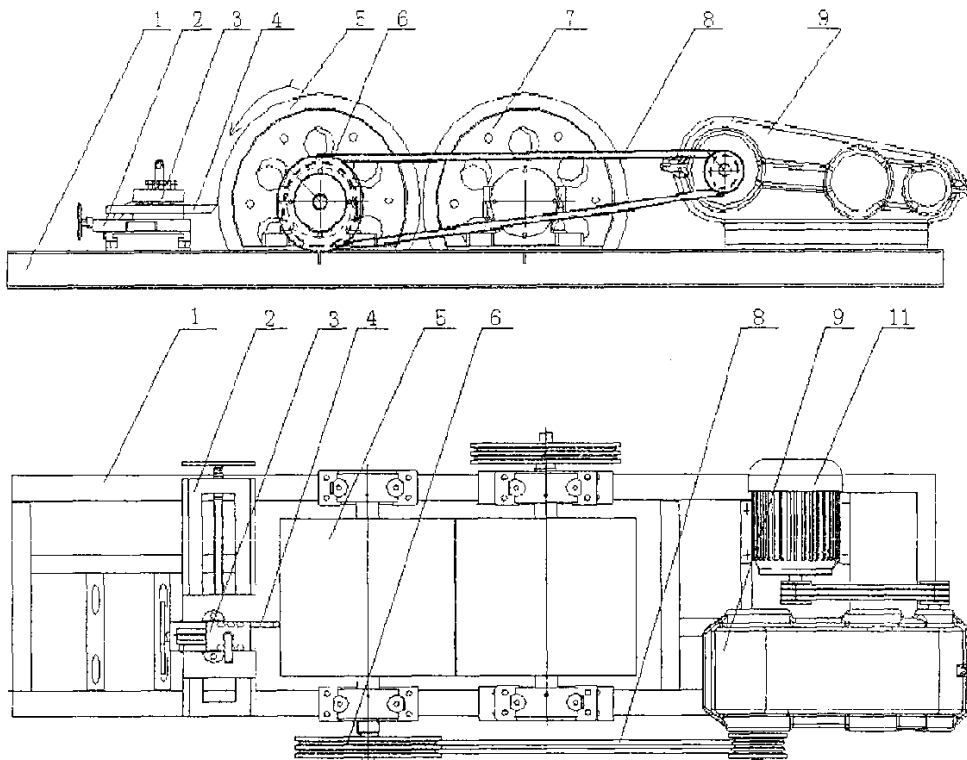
Незнімний ремонтний токарний верстат (20): 1- база верстата, 2- тримач для ножів, 3- нерухомий ніж, 4- токарний інструмент, 5- лівий валок, 6- лівий роликовий шків, 7- правий валок, 8- приводний ремінь, 9- коробка уповільнення, 11- мотор.
